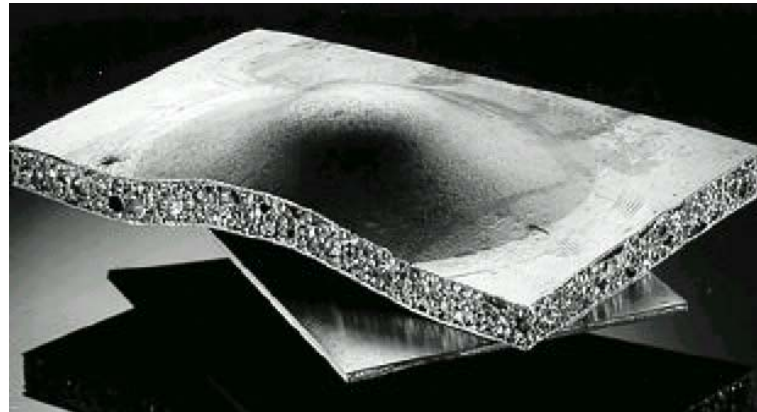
Photographie d'un sandwich aluminium / mousse d'aluminium obtenu par métallurgie des poudres
